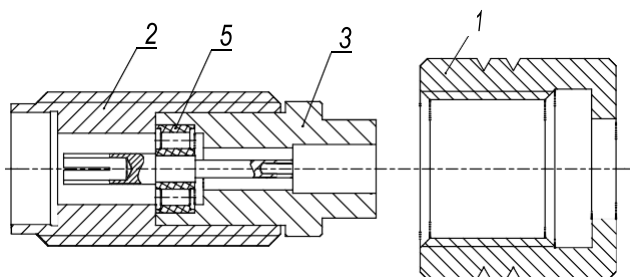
Кабельный соединитель РК1-40-14Р-2 с отсоединенной стягивающей гайкой
